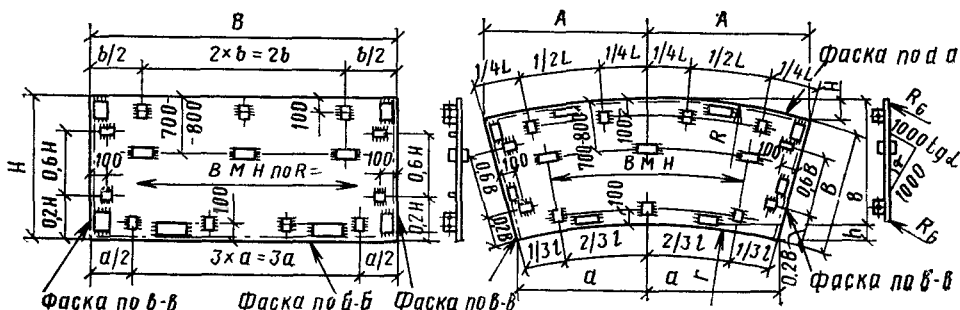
Схема расстановки сборочных шайб и фиксаторов в листовых конструкциях
